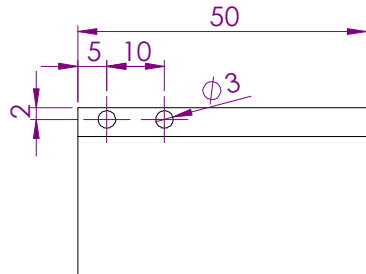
Origineel zie pdf: tussenstuk motor - sheet1
